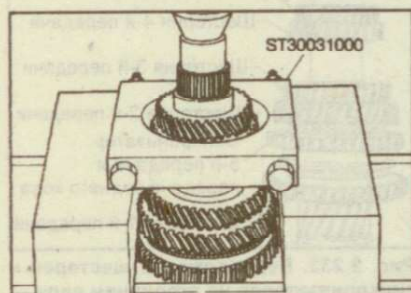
Выпрессовка вторичного вала с шестерни 5-й передачи и шестерни 4-й передачи
